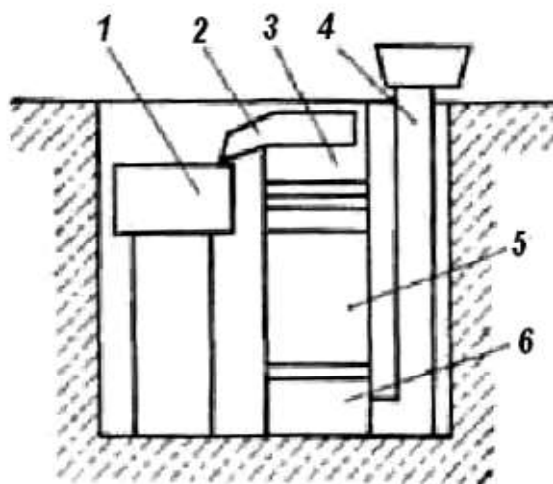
Форма для получения двухслойных валков методом промывки: 1 — емкость для слива вытесняемого чугуна; 2 — сливной желоб; 3 — песчаная полуформа шейки и прибыли; 4 — стояк; 5 — кокиль бочки валка; 6 — песчаная полуформа шейки валка
